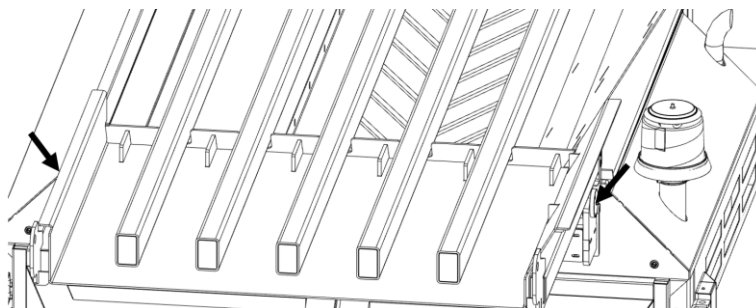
Overzicht smeerpunten rechtse machinedeur, achter schakelkast (43,44)
